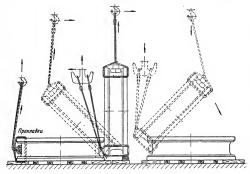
Схема кантовки цилиндрической детали двумя крюками.
